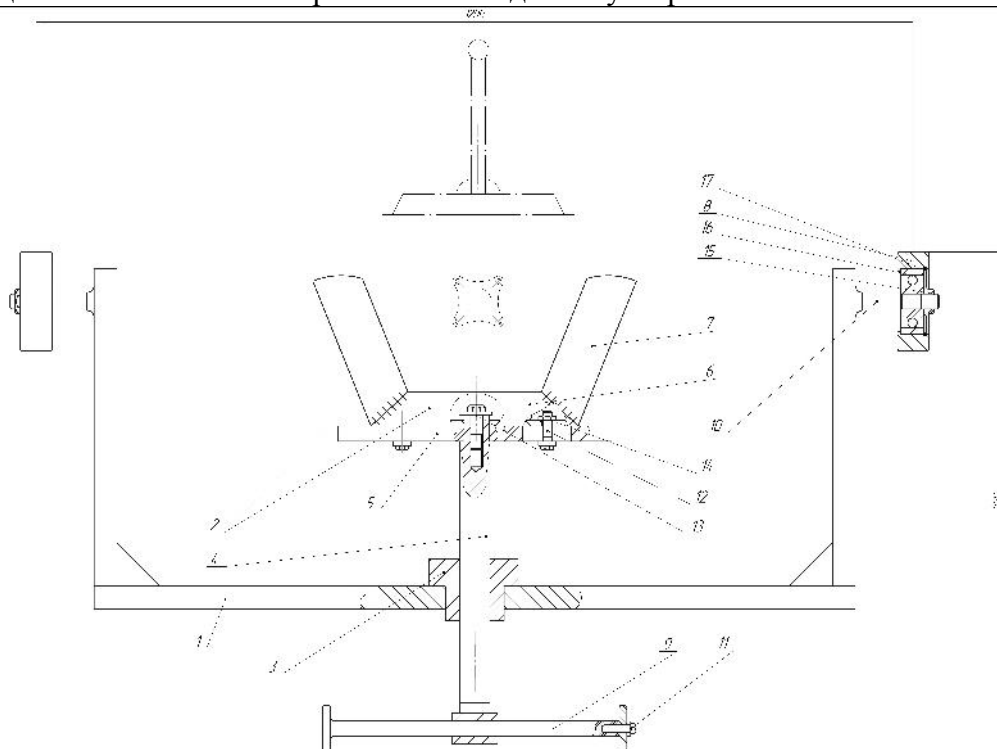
Пересувний візок для зняття і встановлення коробки передач
